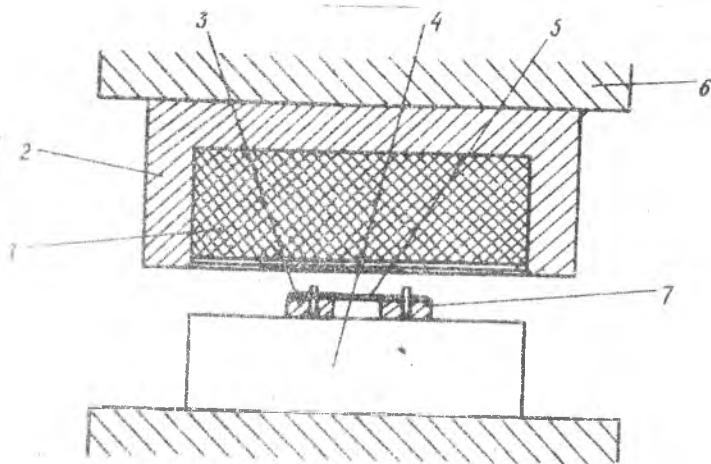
Схема установки для пробивки отверстия эластичной средой
